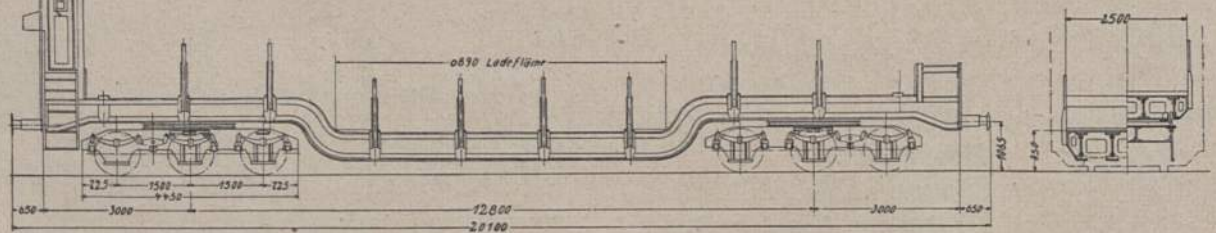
Sechssachsiger Tiefladewagen für 55 t Ladegewicht mit Bremse.
